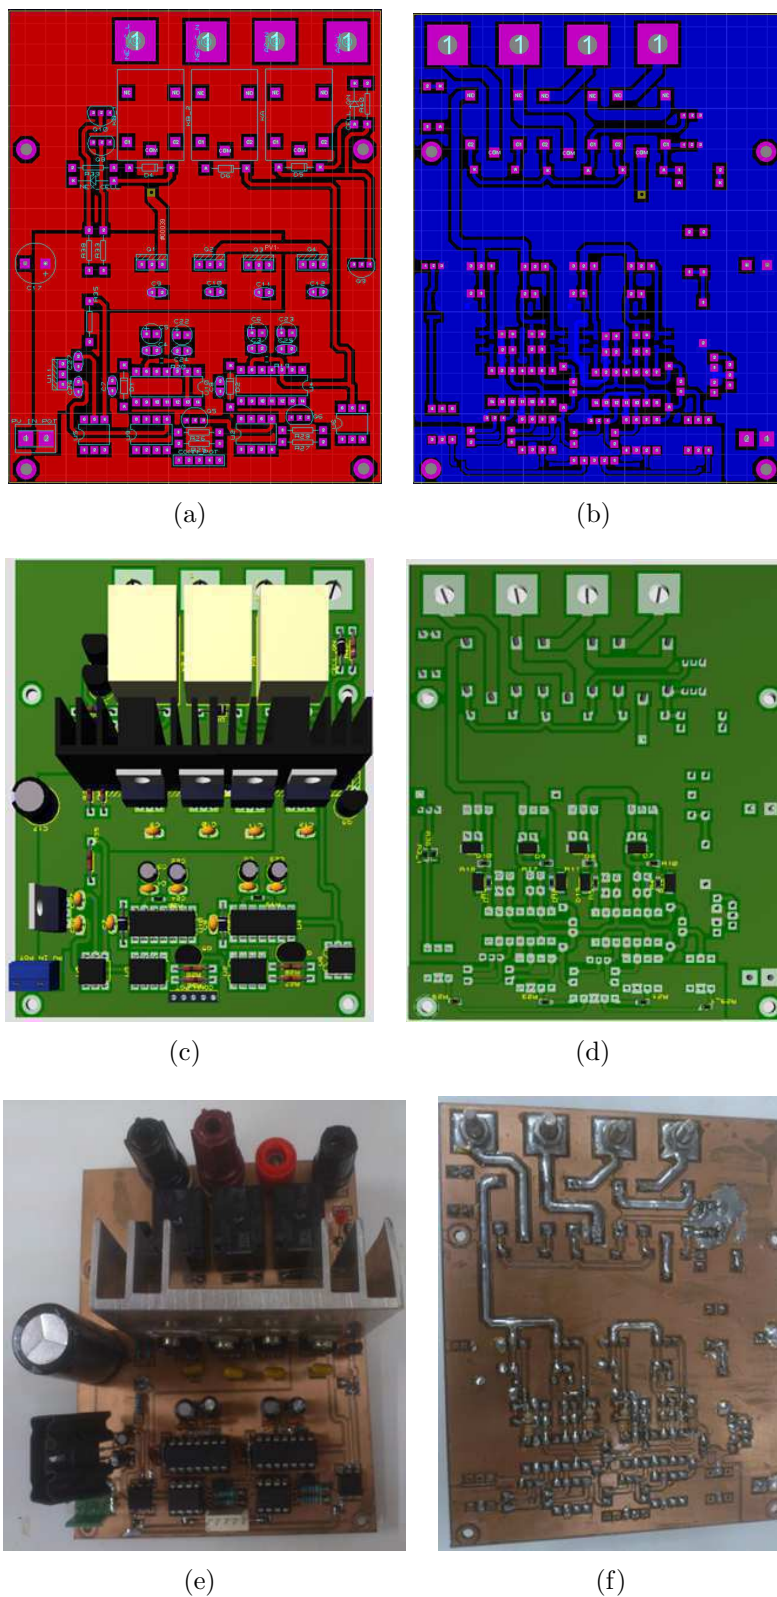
(a) Parte superior e (b) parte inferior do layout da PCB de potência. (c) Visão 3D da face superior e (d) inferior. (e) Foto da face superior e (f) da face inferior da PCB real.
